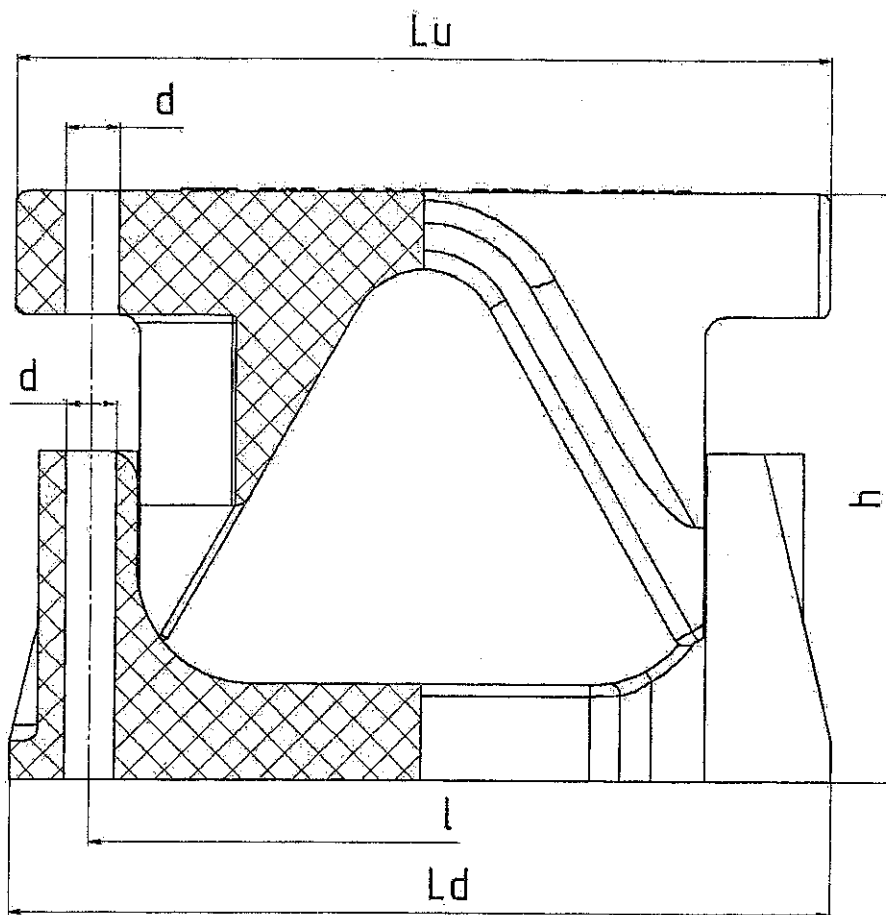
Габаритные размеры и внешний вид универсального кабельного крепления марки УККЗ
